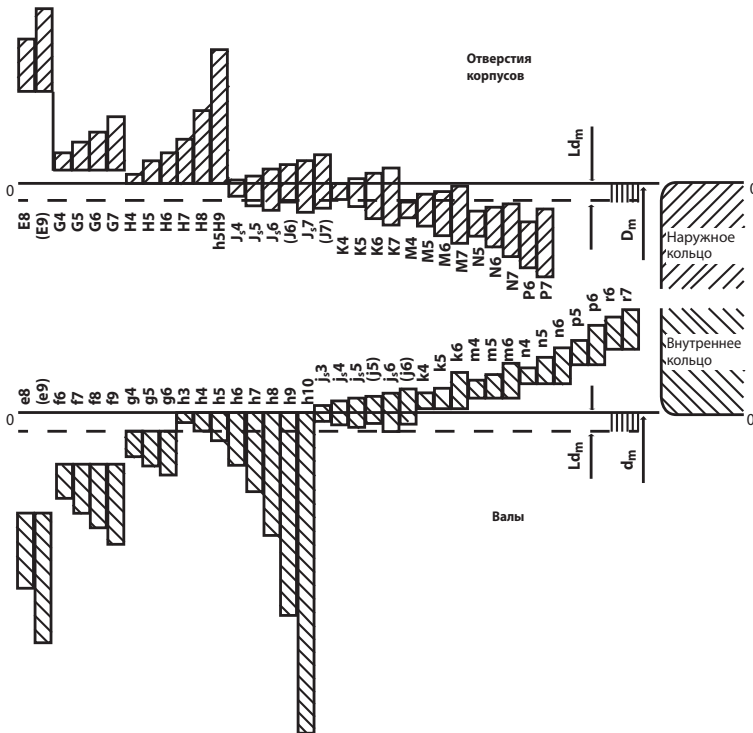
Схема расположения полей допусков при посадках подшипников на валы и в отверстия корпусов
